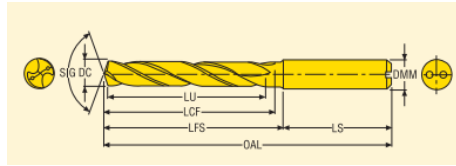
Свердло SD205A-0800-043-08R1-P [10, с.52]
